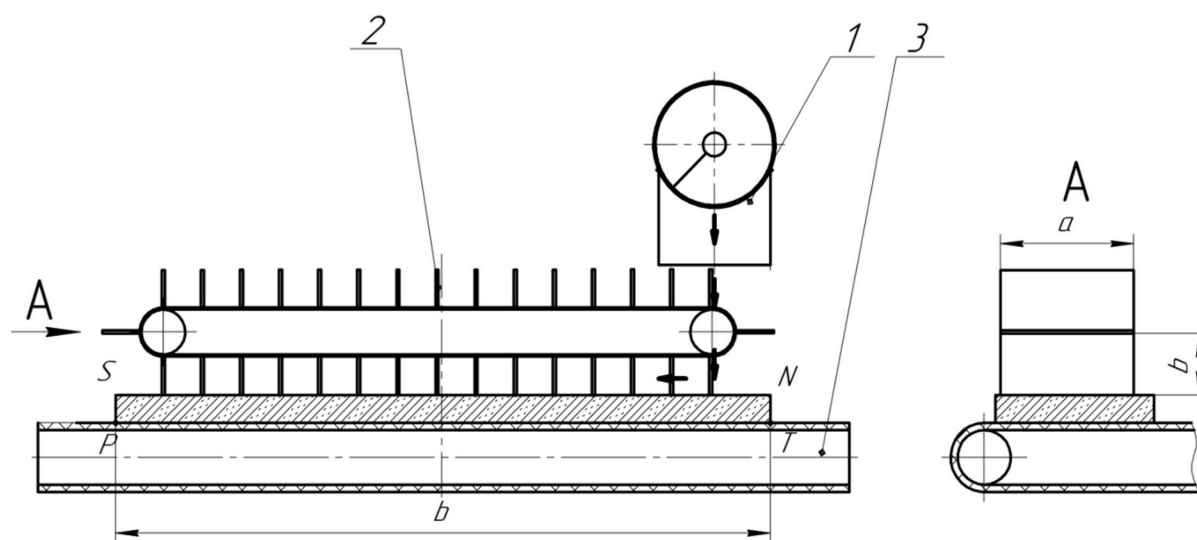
Схема работы скребкового разравнивающего устройства и ленточного транспортера:
